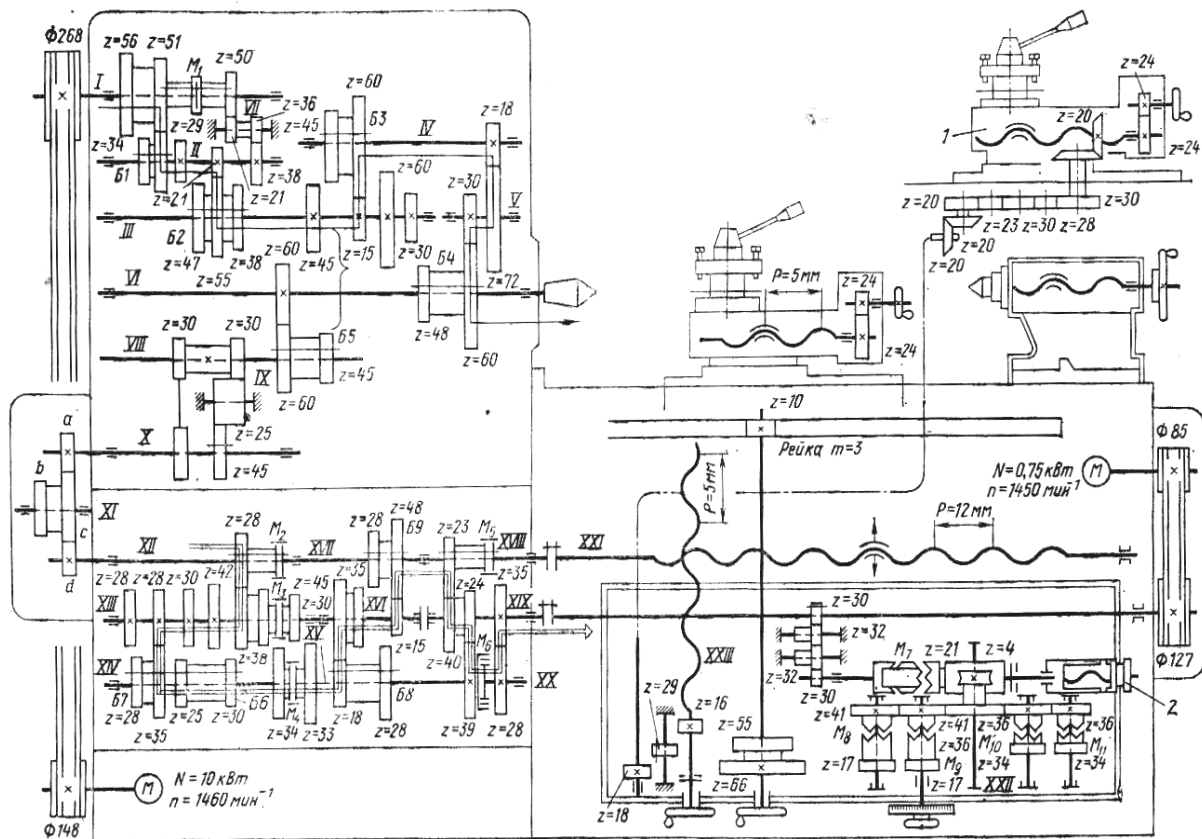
Кинематическая схема токарно-винторезного станка модели 16K20
